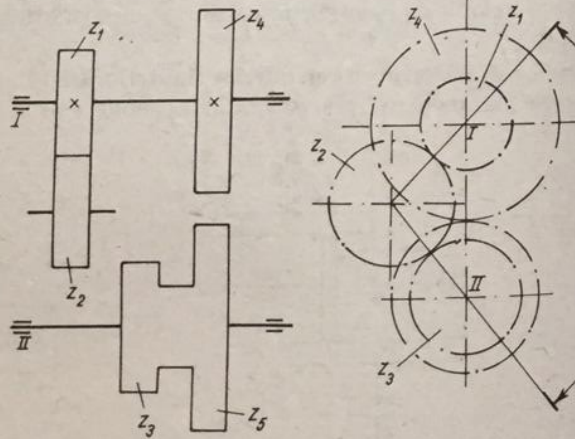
Mecanism inversor cu bloc dublu balador.
